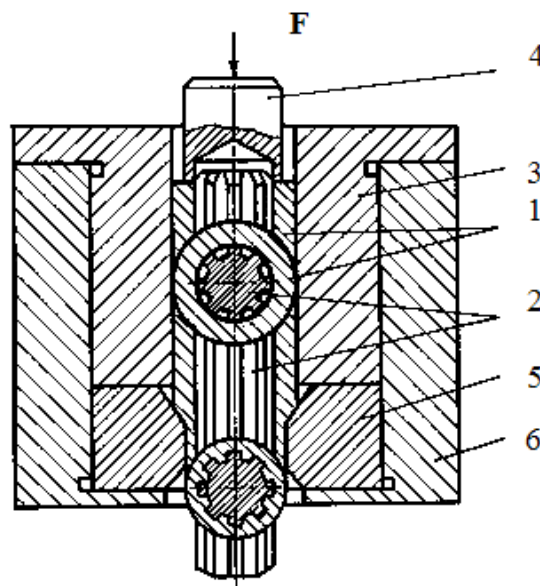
Схема процесу формоутворення внутрішніх шліців в трубних заготовках
